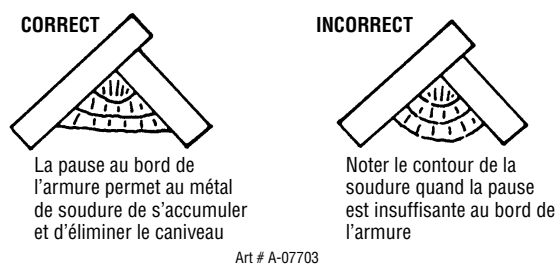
Exemples de soudures de joint vertical
